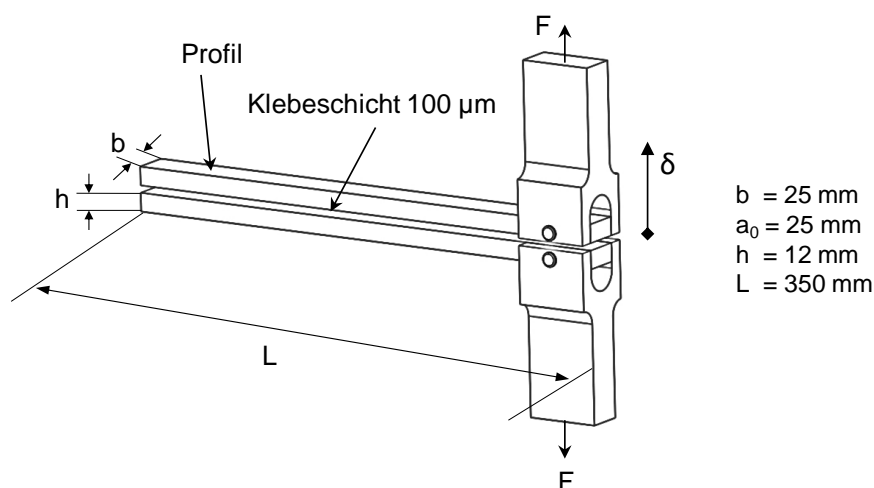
Aufbau und Abmessungen des *Double-Cantilever-Beam*-Test (DCB)
